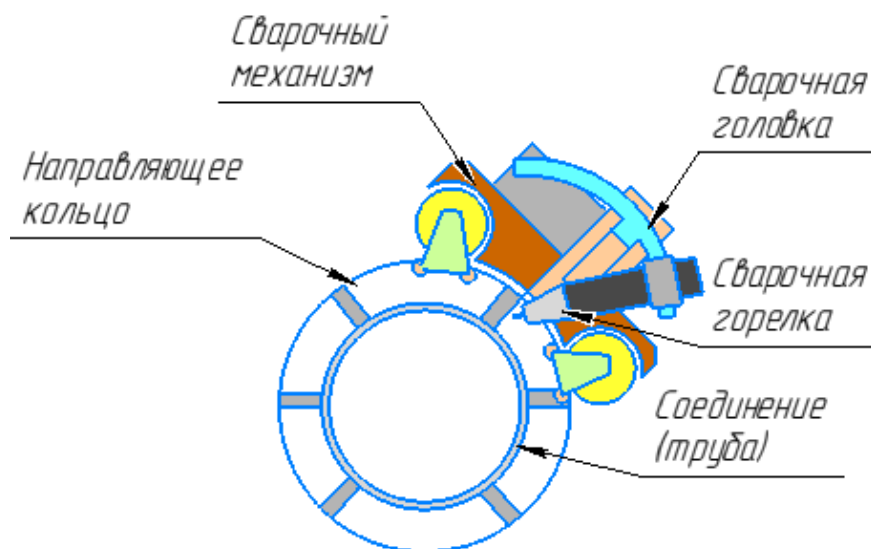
Схема установки системы для орбитальной сварки [5]
